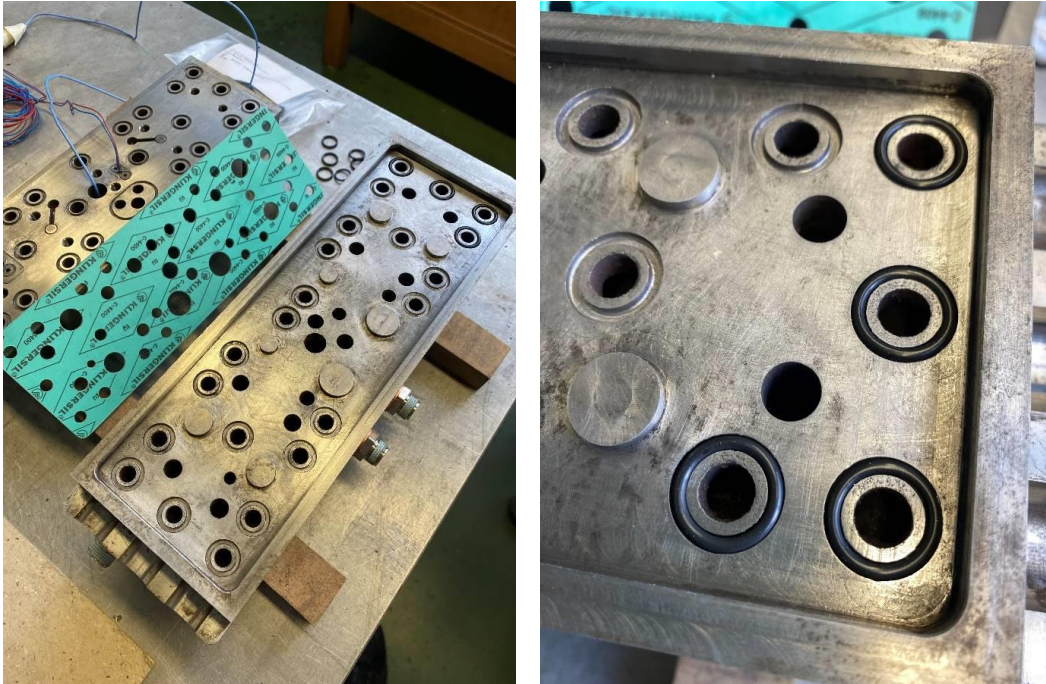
Nacharbeit mit O-Ringen am Versuchswerkzeug 1 gen. Testkörper
